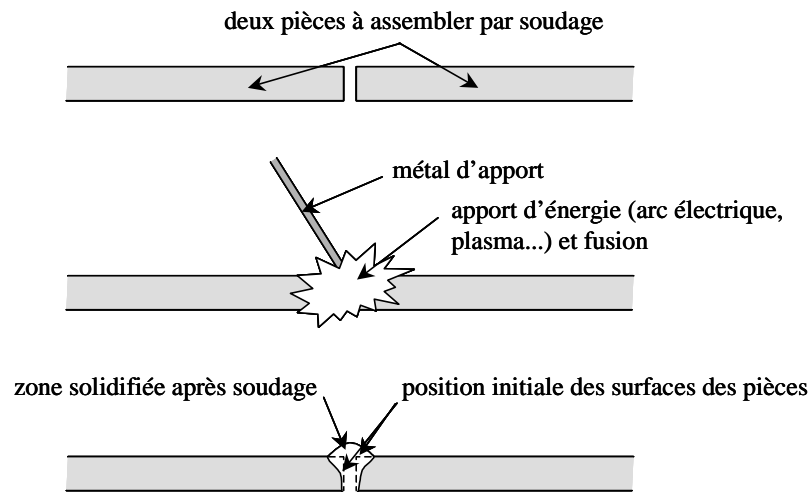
Principe du soudage. Noter la différence avec le brasage : la fusion locale des pièces à assembler
